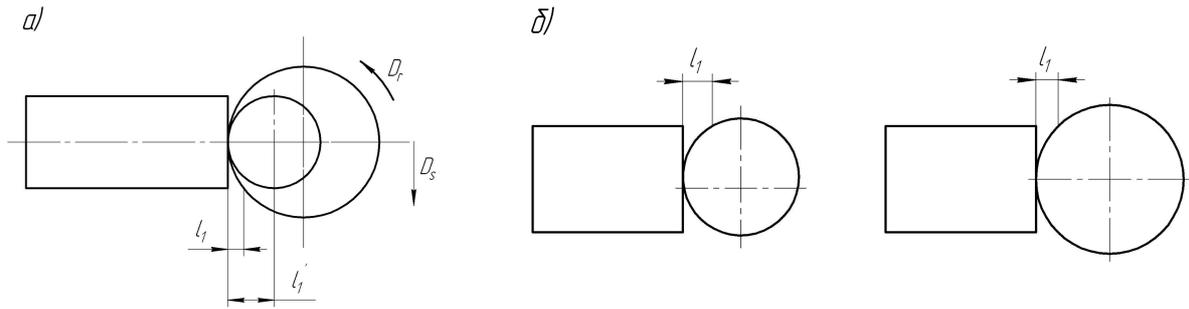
Схема фрезерования поверхности торцовой фрезой с различными диаметрами (а) и изменением размера врезания (б)
